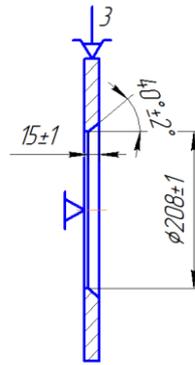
Эскиз базирования заготовки на 005 токарной операции.
